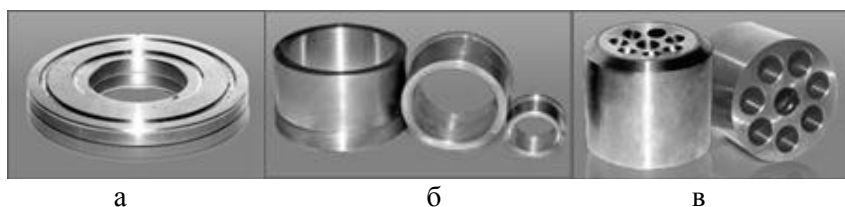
Приклади деталей, виготовлених з біметалів:
